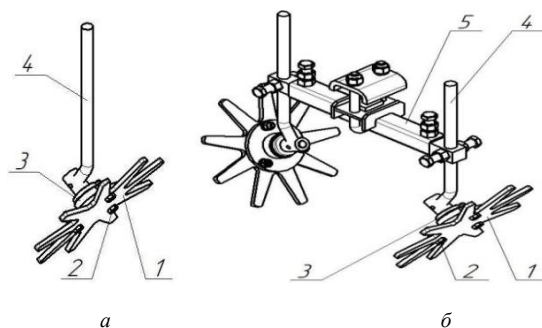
а – фрезерный лучеобразный диск; б – секция фрезерных лучеобразных дисков для обработки боковых поверхностей гряд
